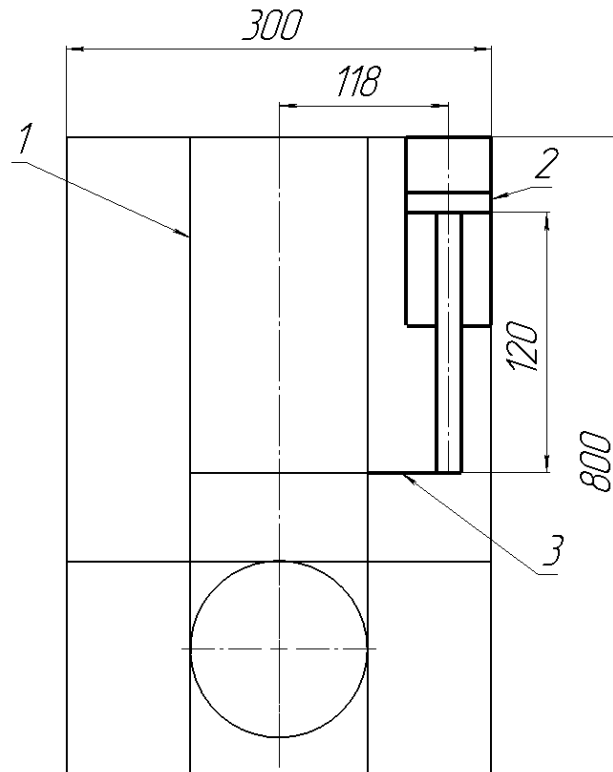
Розрахункова схема встановлення пневмоциліндру, вид зверху: 1 – шліфувальний вузол; 2 – пневмоциліндр; 3 – кронштейн.
